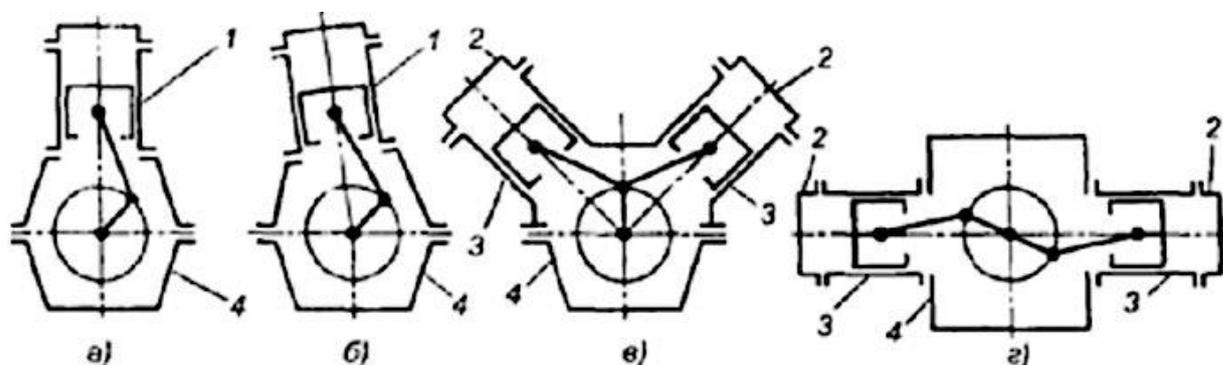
Варианты расположения цилиндров ДВС:
